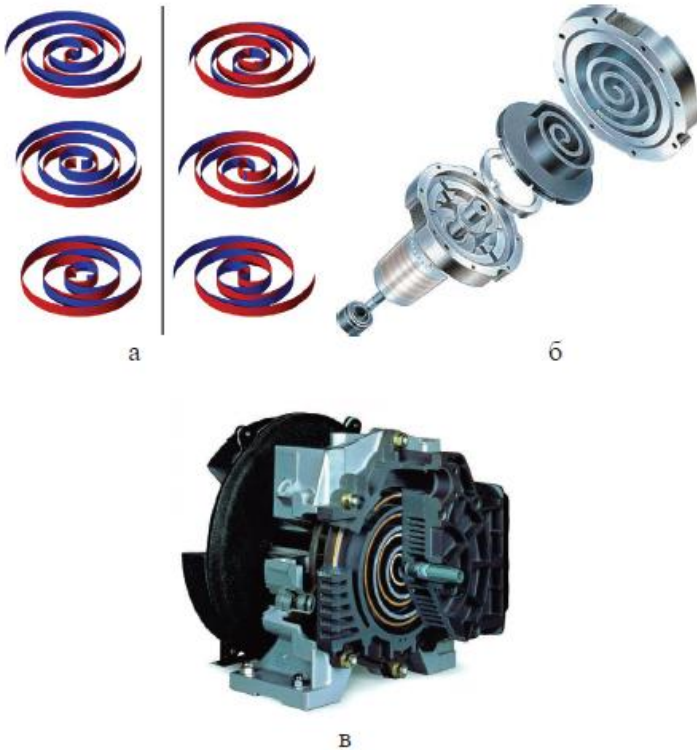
Спиральний компресор: а – схема роботи спірального компресора; б – конструкція робочого органу; в – зовнішній вигляд у розрізі спірального компресора
